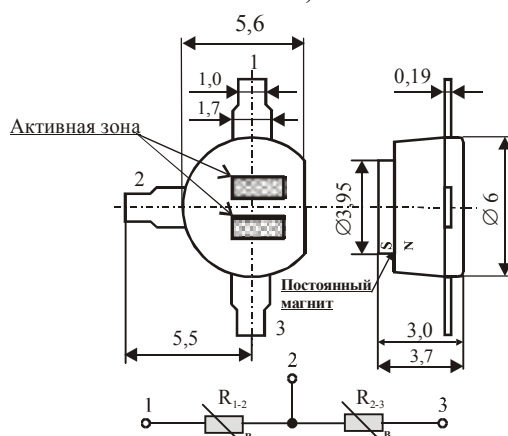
Внешний вид и габаритные размеры магниторезисторов FP 212 L 100-2, FP 212 D 250-2
